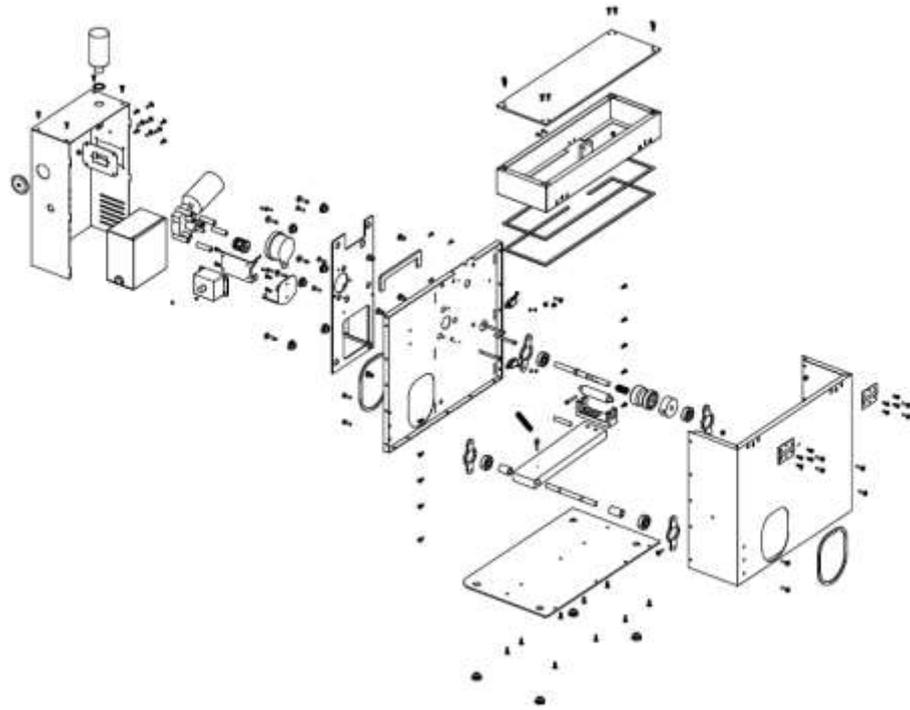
Explosionado OxyGEN-IP. Fuente: Exploded, 2020.
